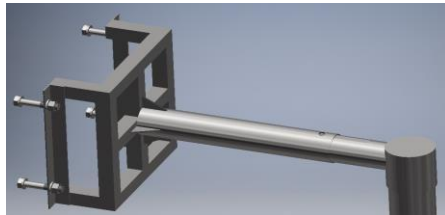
Soporte y guía de la columna. Fuente: Autores.
